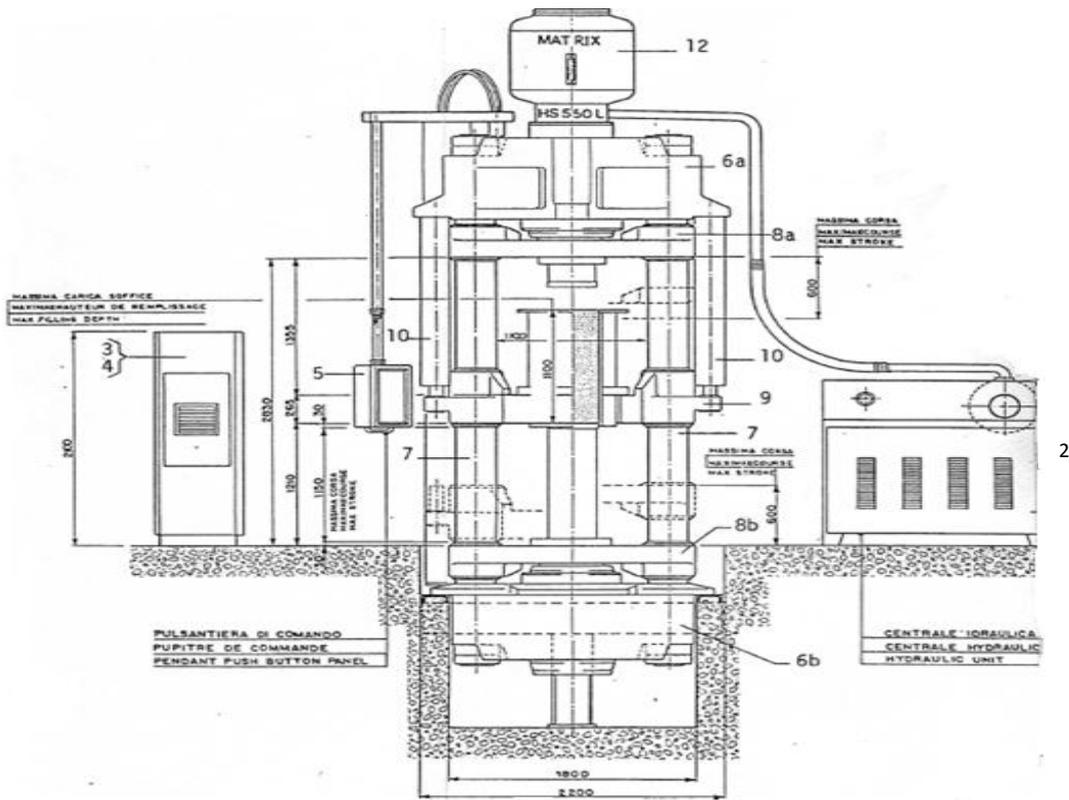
Vue de face de la presse MATRIX HS 550L [3].
